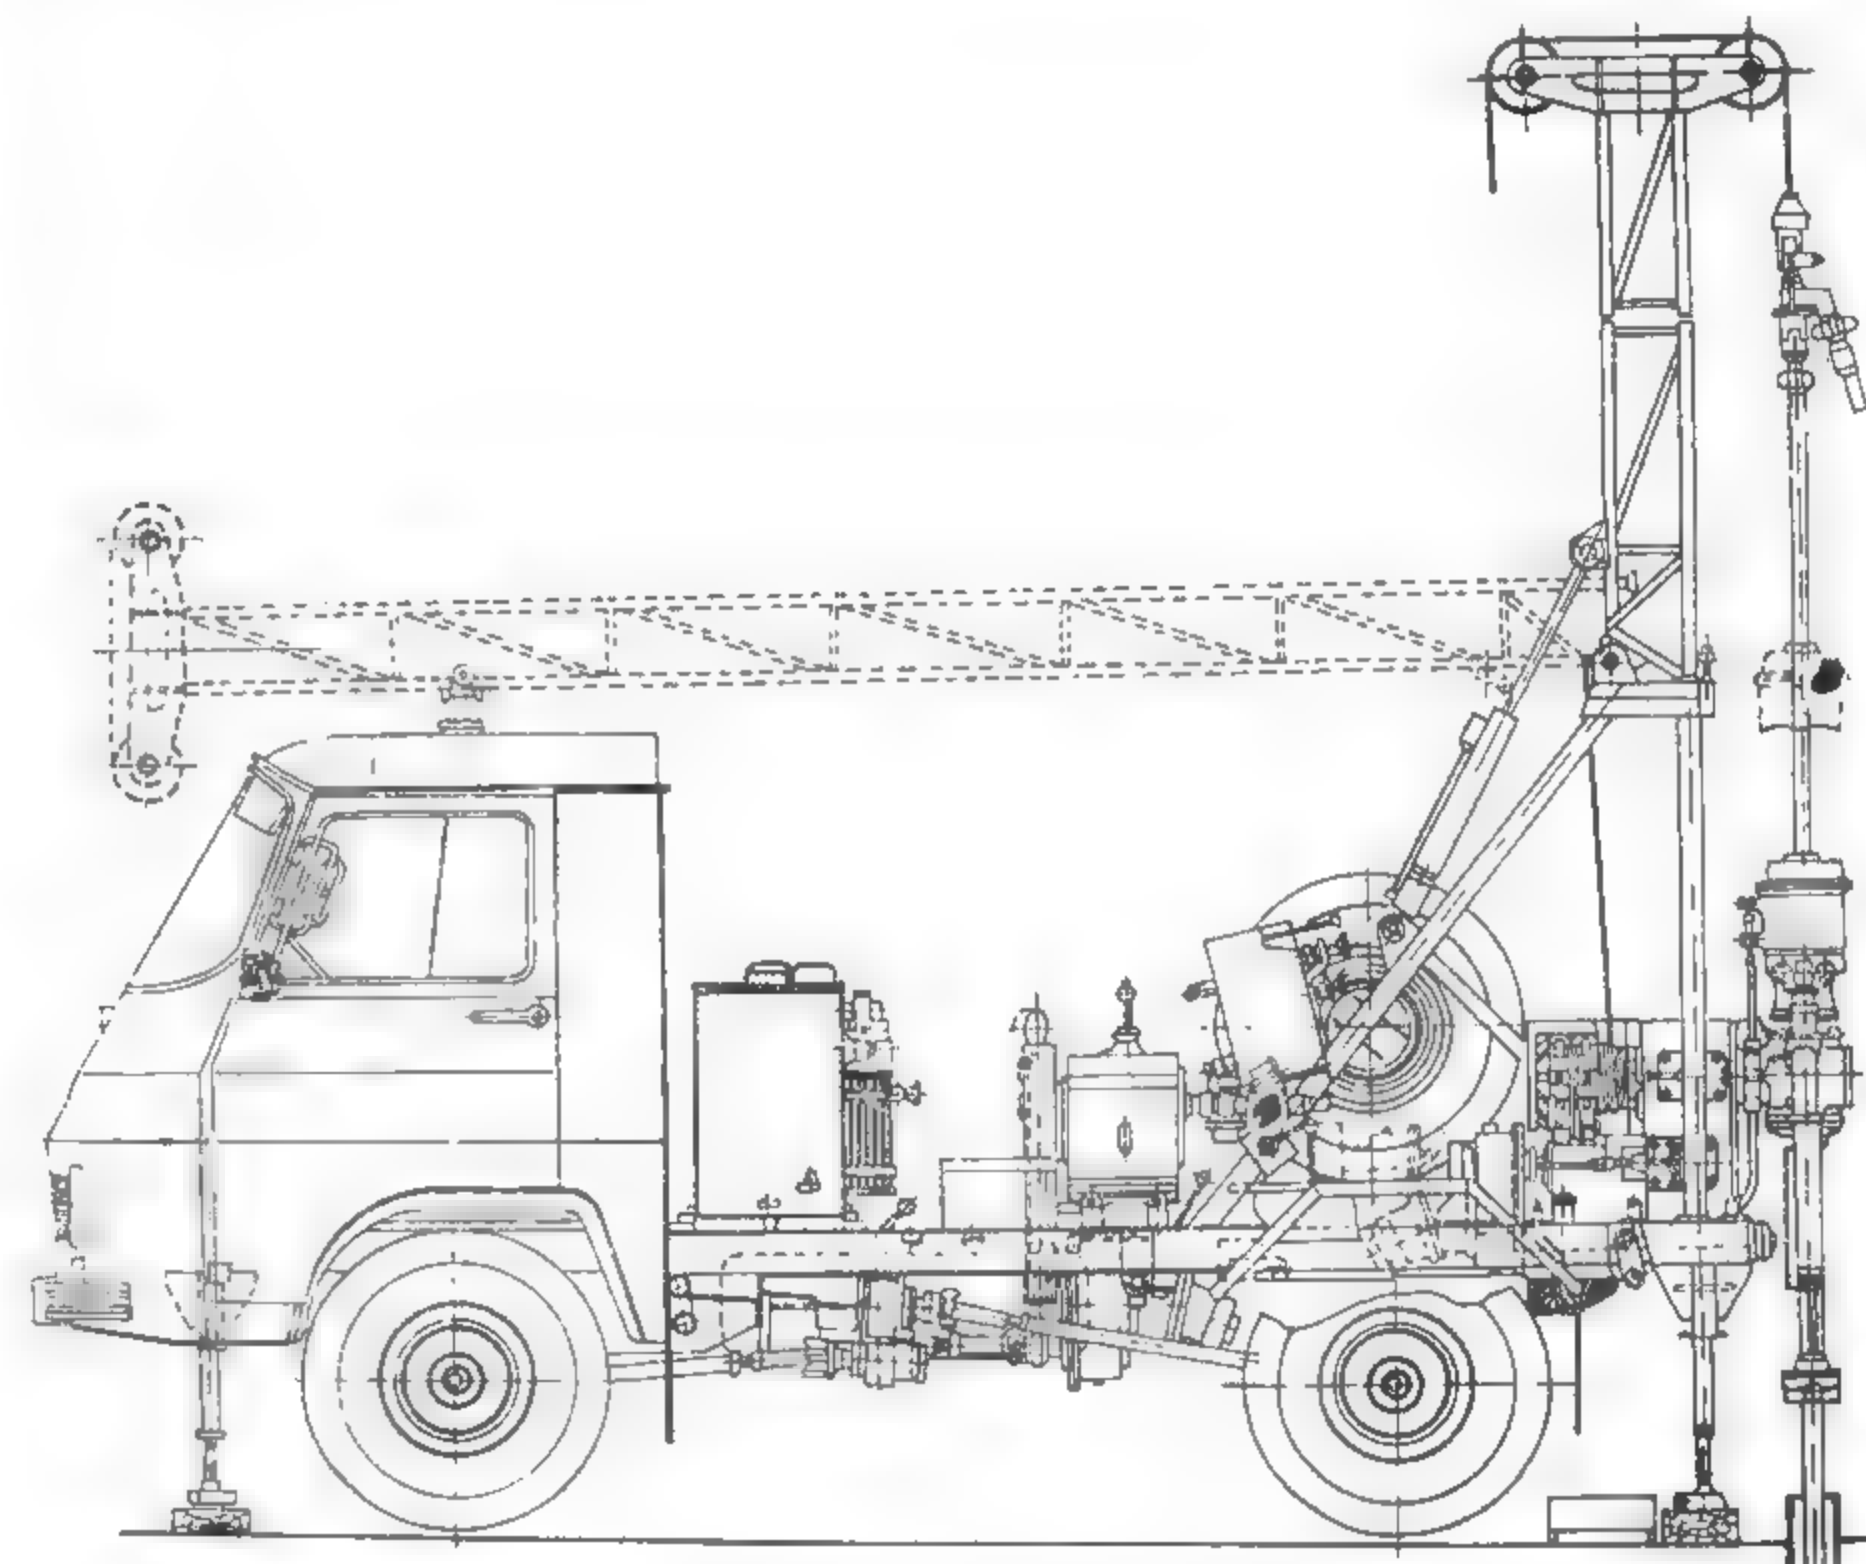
Instalația de foraj SG-150 autotransportabilă (varianta I).
